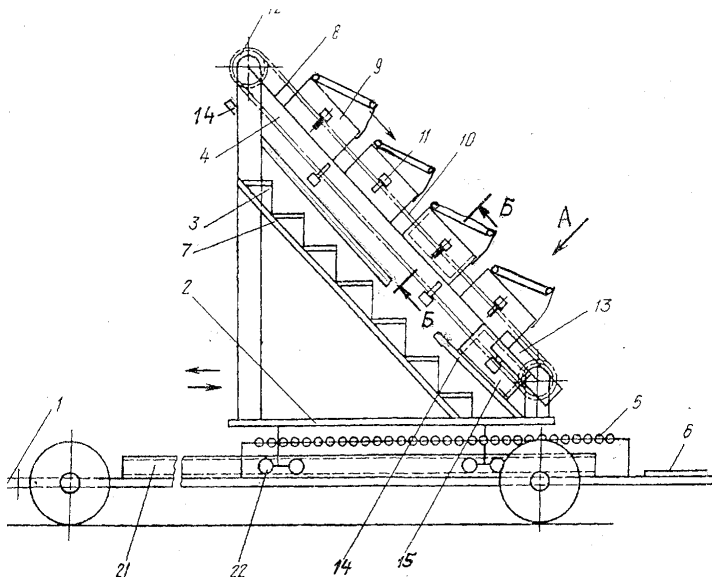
Платформа для сбора плодов, общий вид сбоку
